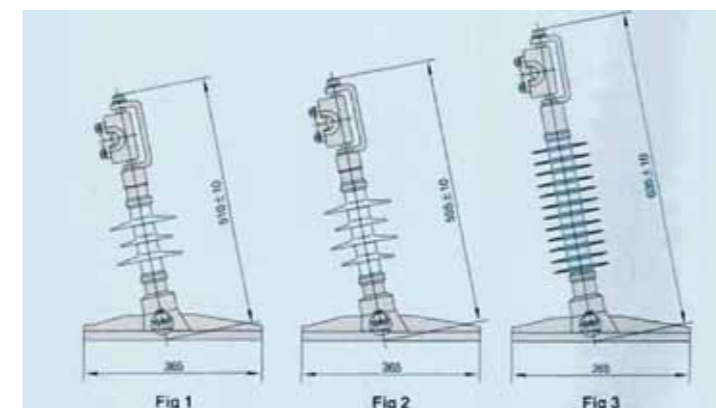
Внешний вид и размеры линейных штыревых изоляторов
